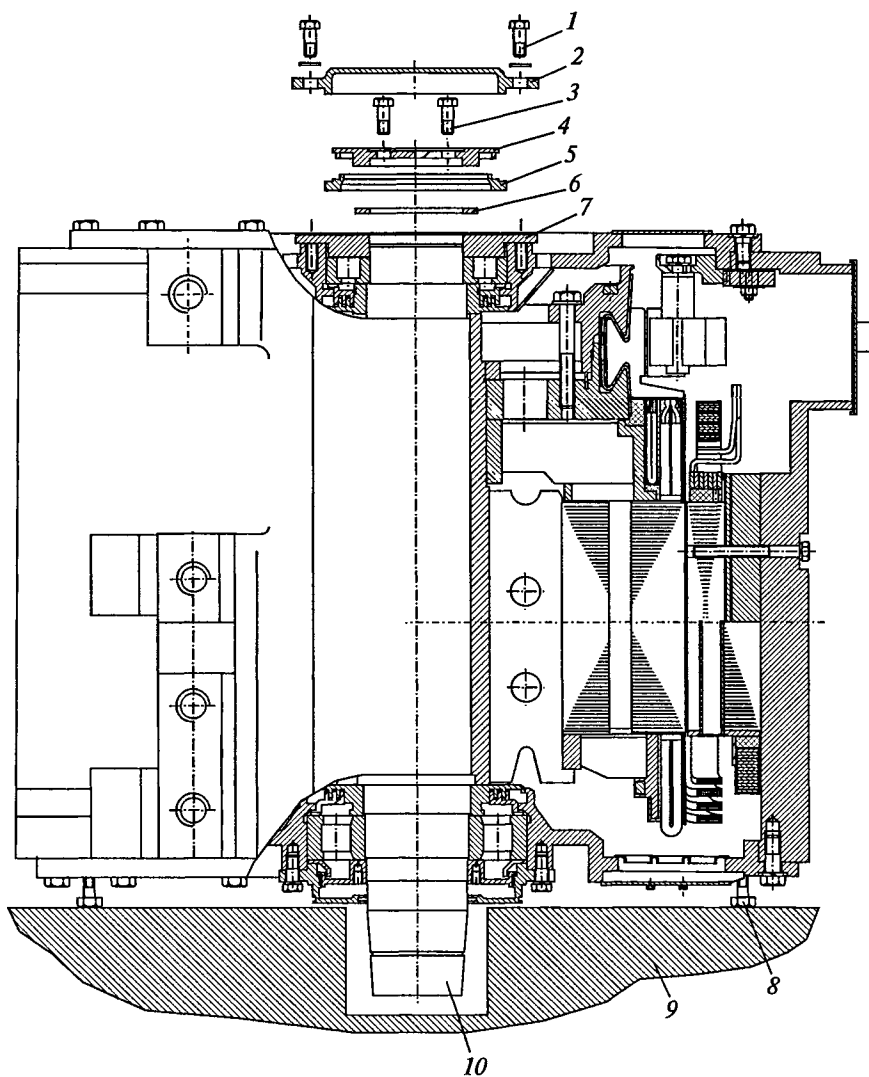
Разборка малого подшипникового щита ДТК-800КЭ:
